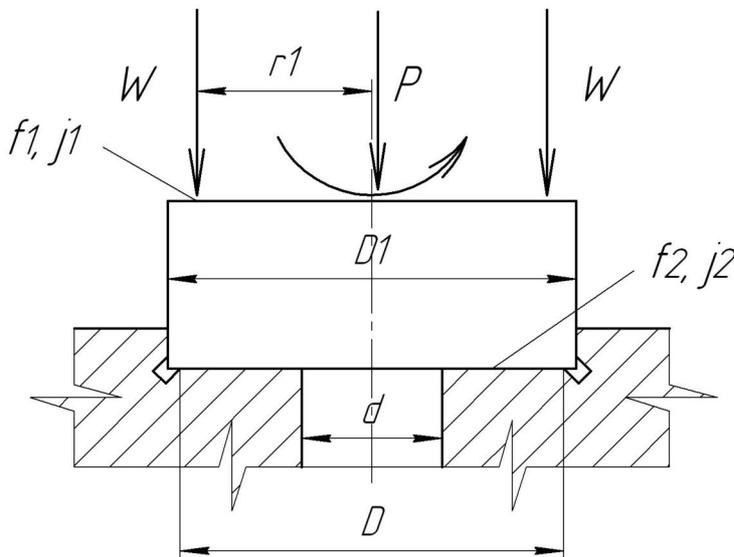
Схема сил действующих на заготовку при ее установке по наружной поверхности
